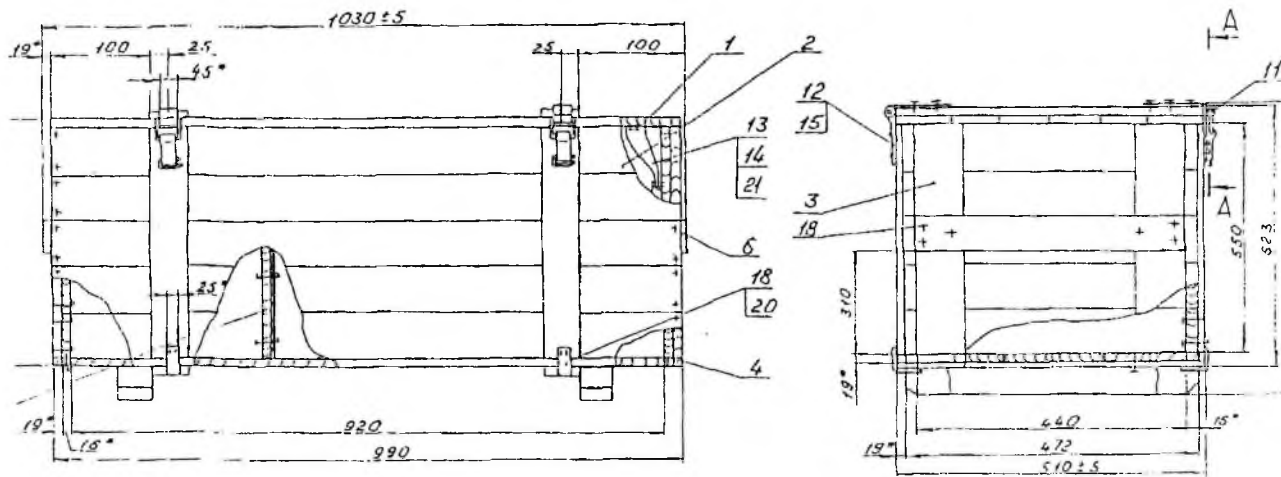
Деревянная тара с откидной крышкой для упаковки имущества (электронасос, резервуар для приготовления раствора, материалы и т.д.) станций СКО-0,3 БС и СКО-0,3 («Шатер»)
